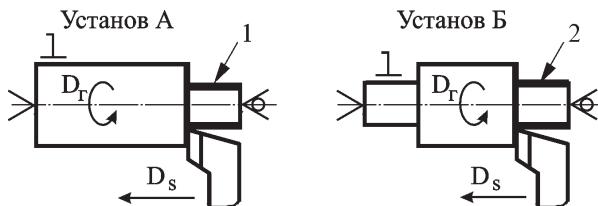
Схема обработки поверхностей 1 и 2 вала за два устанока
